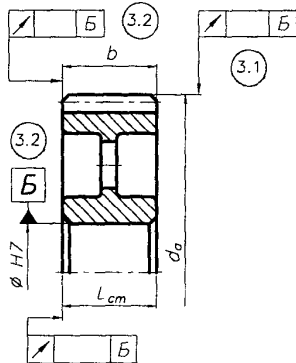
Указание допусков формы и расположения поверхностей зубчатого колеса
